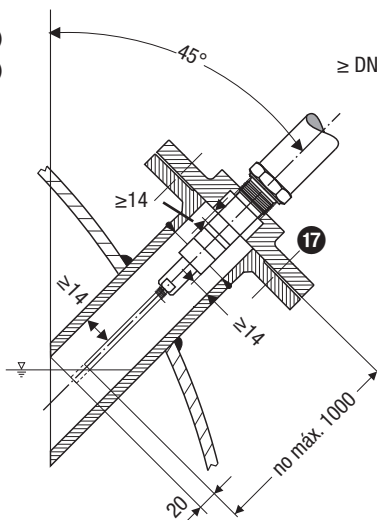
Montagem inclinada, por ex., em caldeiras de vapor
